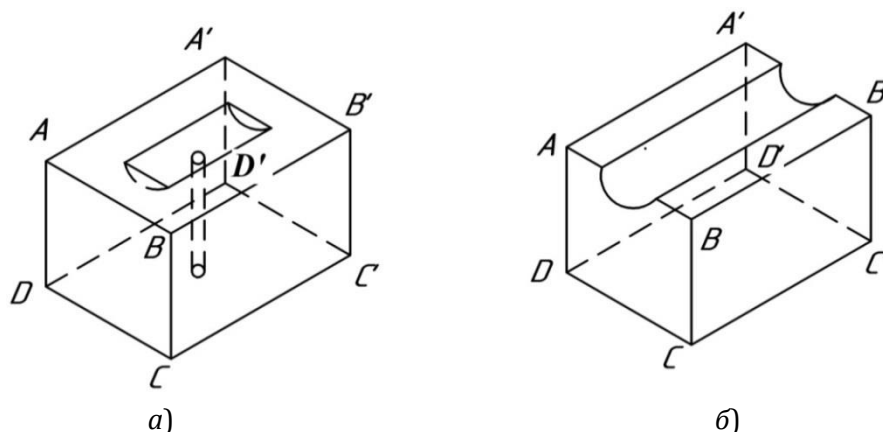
Типы матриц для сварки взрывом с одновременной штамповкой цилиндрических изделий:
